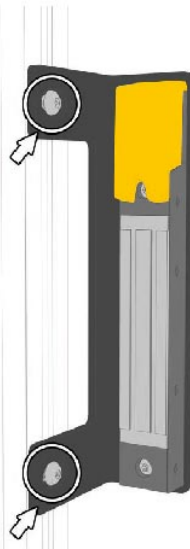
Montageplatte mit Prozesszuhaltung am Profil anbringen und und Schrauben M8 x 12 mm Torx festziehen.
